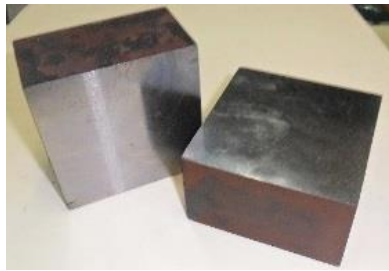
Material usinado no Processo de Usinagem por Fresamento deste trabalho.
